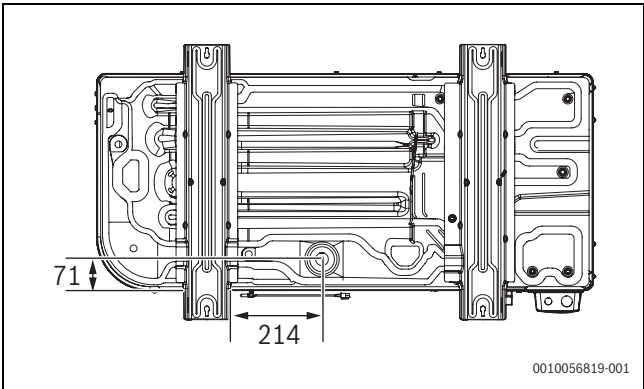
Abmessungen der Wärmepumpe, Ansicht von unten
